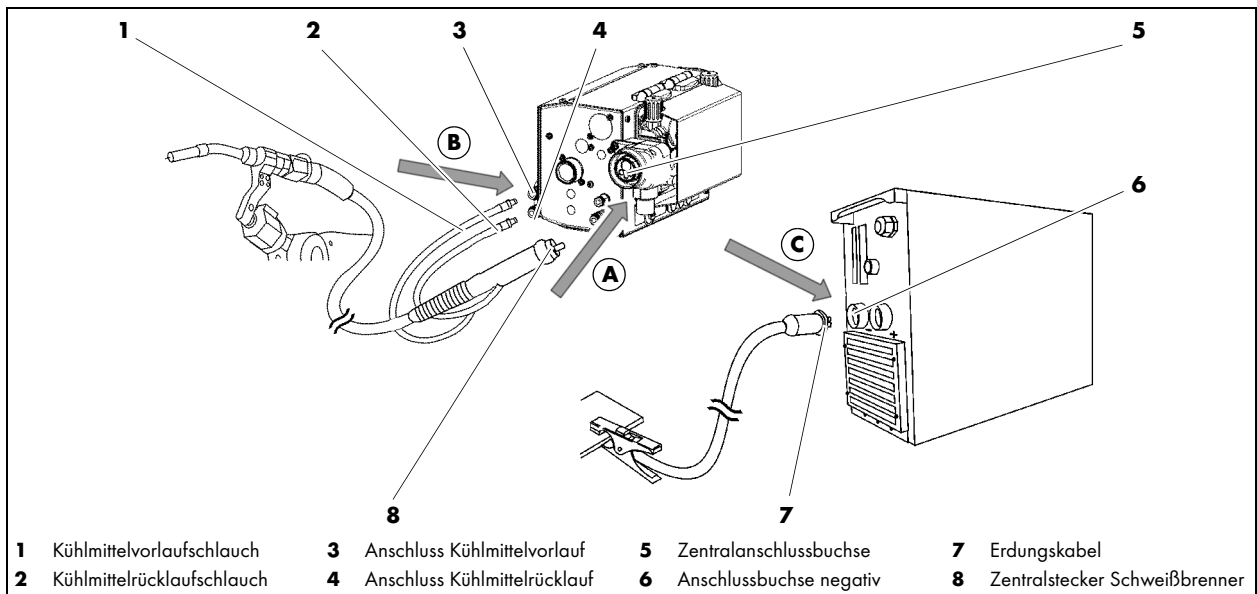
Schlauchpaket Schweißbrenner (Euro-Zentralanschluss) iROB Feed 22 (Version mit Drahtvorschub rechts montiert)
